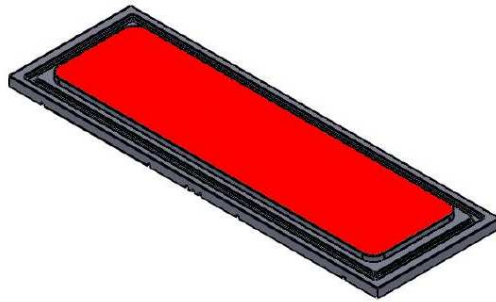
Face superior da placa de aço inox 316L usinada com a região a ser revestida em vermelho.
